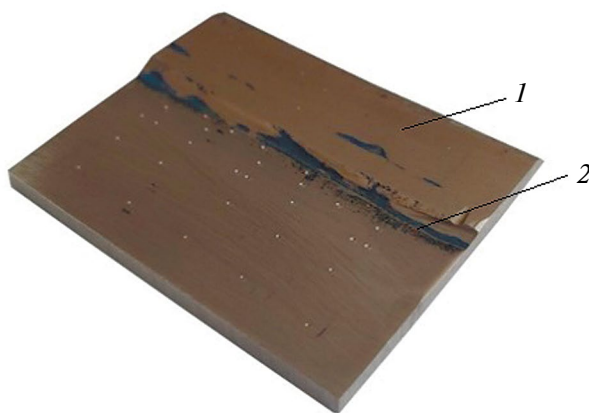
Натурный образец для испытаний: 1 — наплавленная область; 2 — основной металл.
